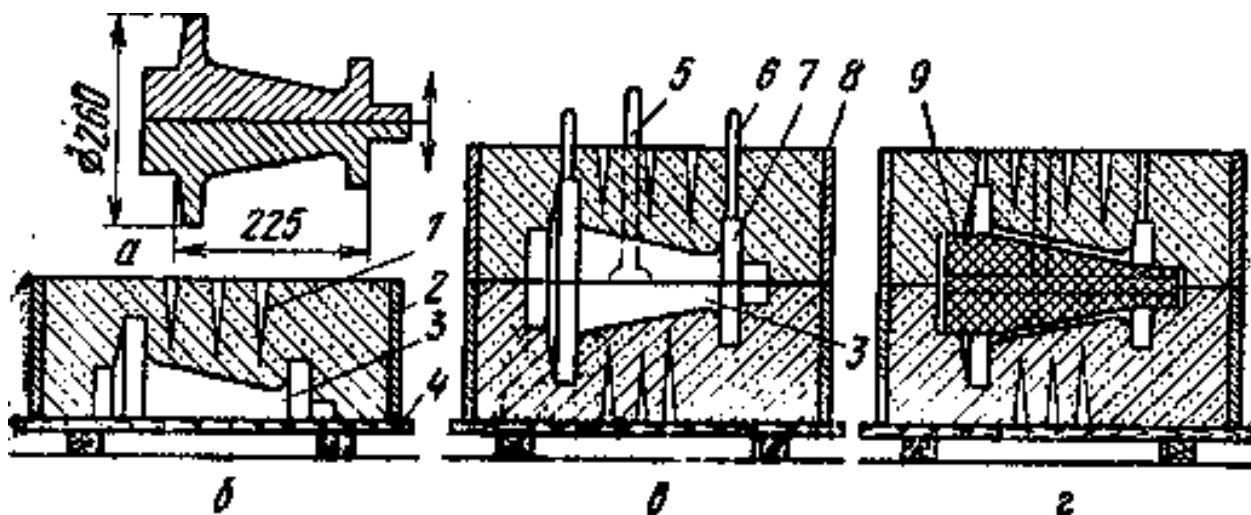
Схема формовки в двух опоках по разъемной модели:
